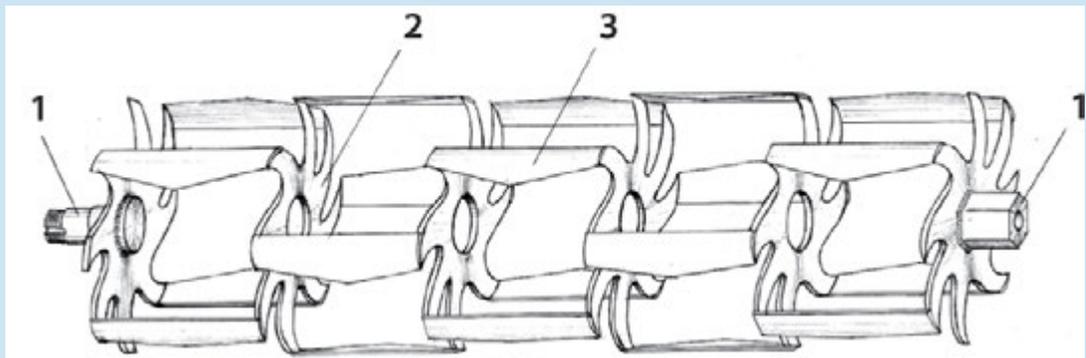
Фрезерный барабан: 1 – цапфа; 2 – дисковая фреза; 3 – режущий нож
